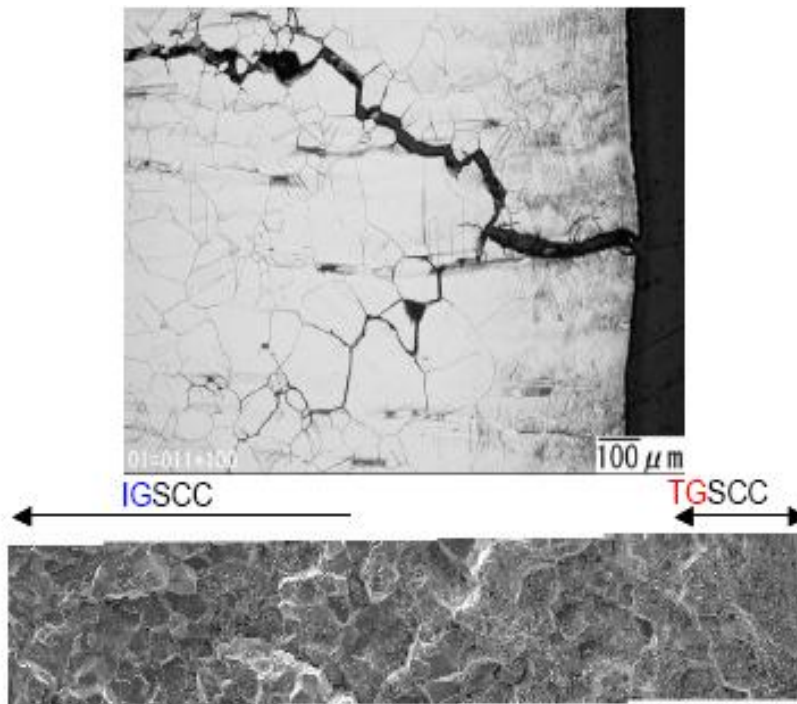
Agrietamiento en el material base de la soldadura H6 en una planta Japones (Después de Susuki *et al.*)²⁸
